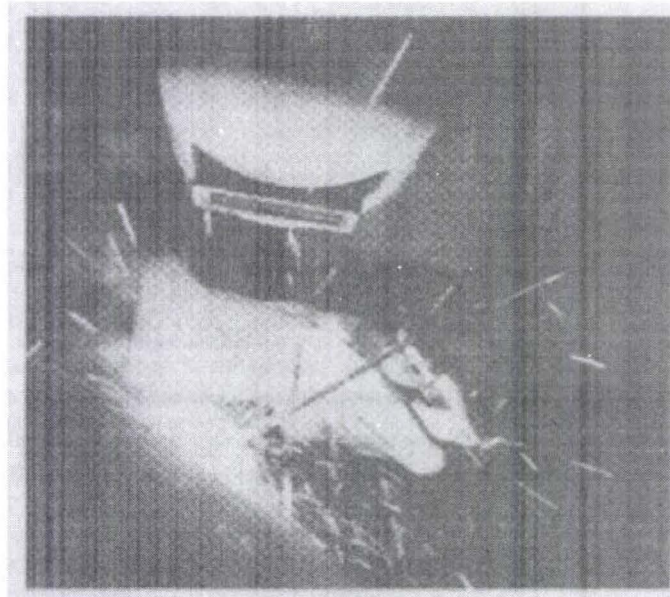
Soldadura metálica con arco protegido (soldadura de varilla) ejecutada por un soldador<sup>142</sup>
